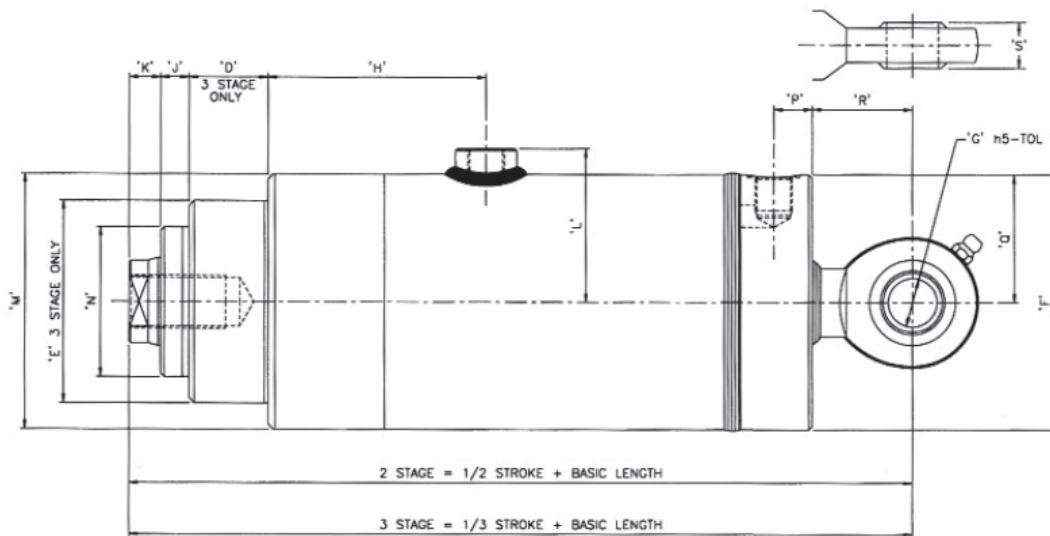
Extracto del catálogo del fabricante del cilindro hidráulico. Representación de dimensiones.
